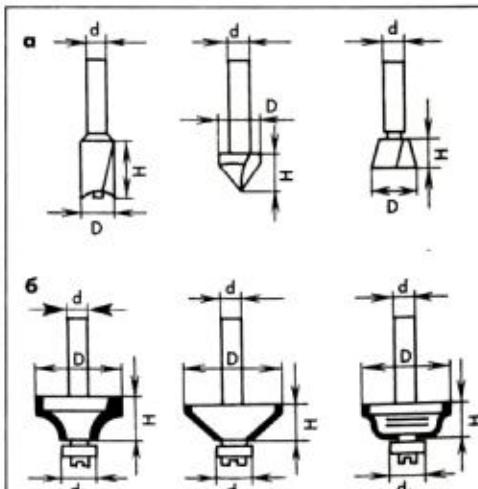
Фрезы для фрезерования ручным электрофрезером:
